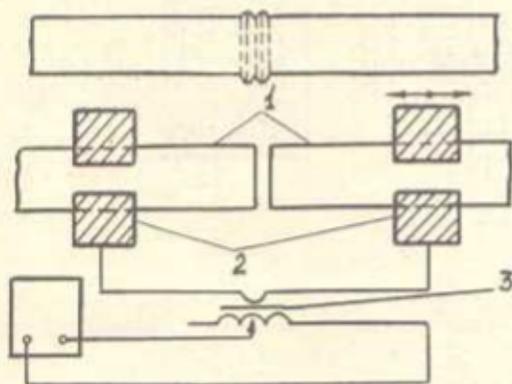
Контактная стыковая сварка: 1-детали; 2-зажимы; 3- сварочный трансформатор
